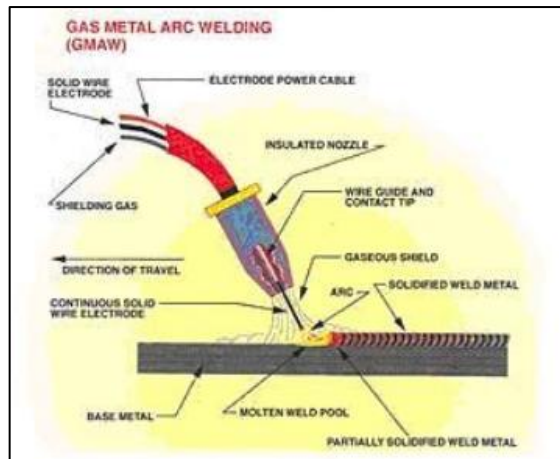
3: Diagrama esquemático del proceso de soldadura GMAW
